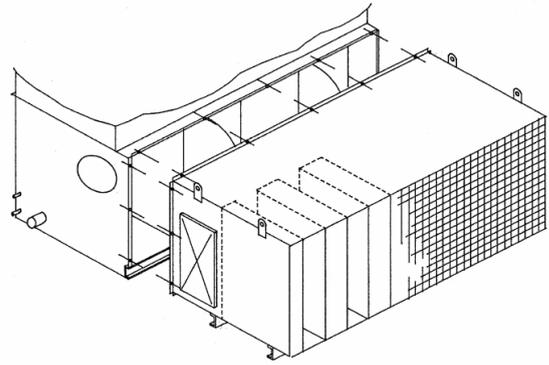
Detailzeichnung zum Einbau des Einlass-Schalldämpfers
